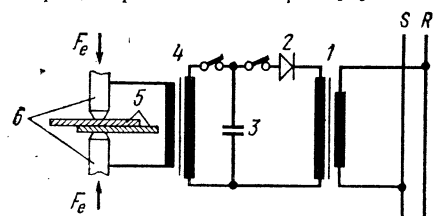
Импульсная конденсаторная сварка:
